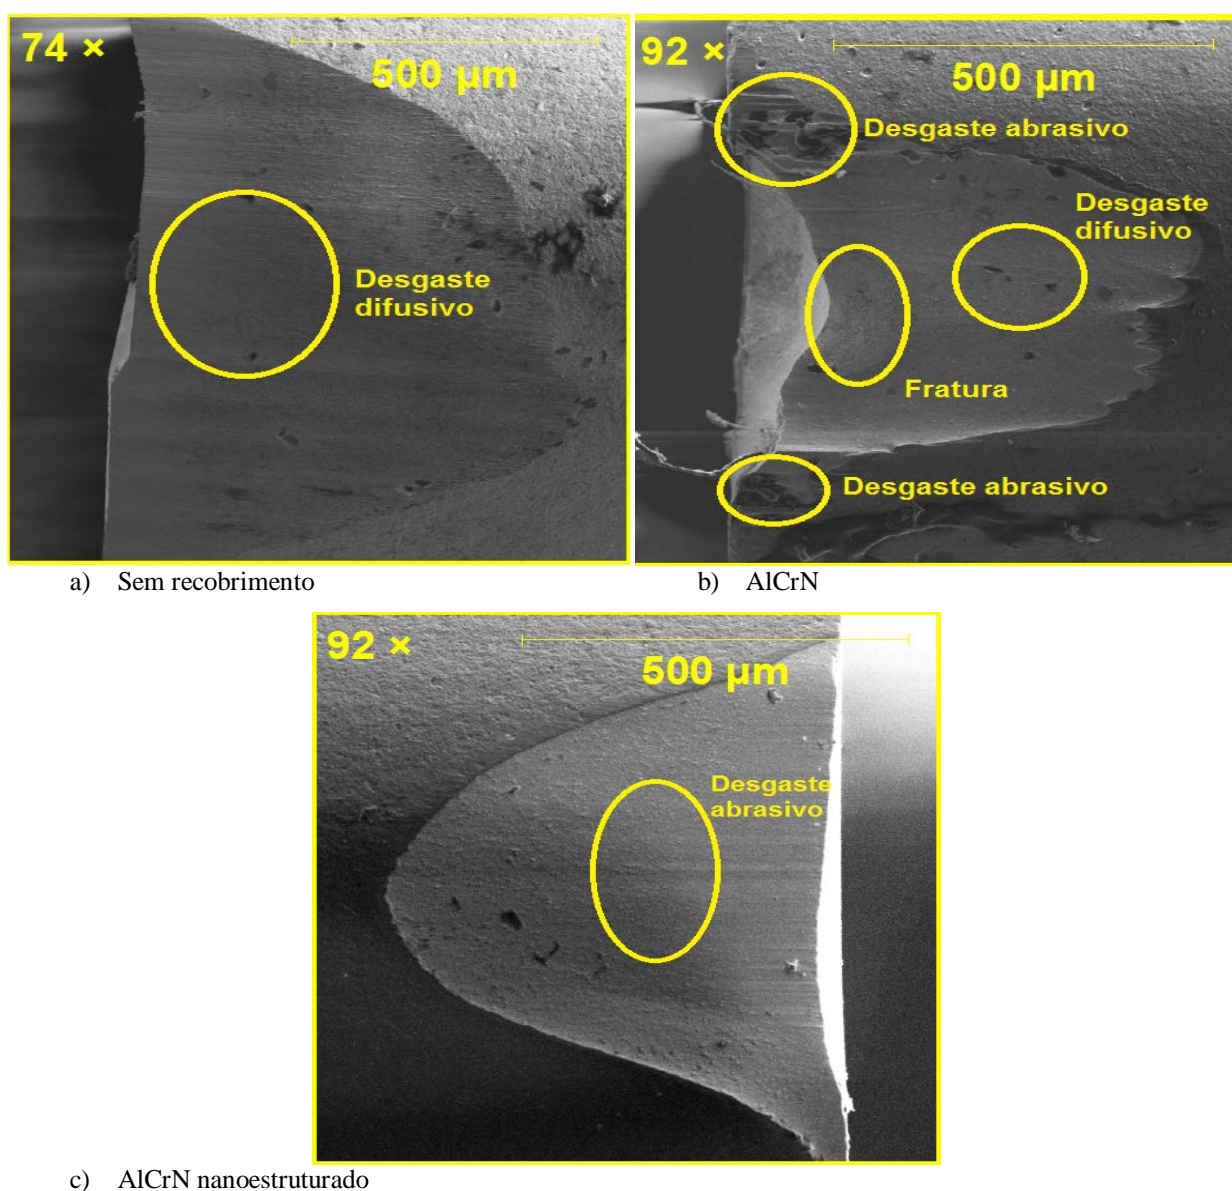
Superfícies de folga das ferramentas após o torneamento com velocidade de corte de 200 m/min, avanço de 0,10 mm/rev e profundidade de usinagem de 0,25 mm.
